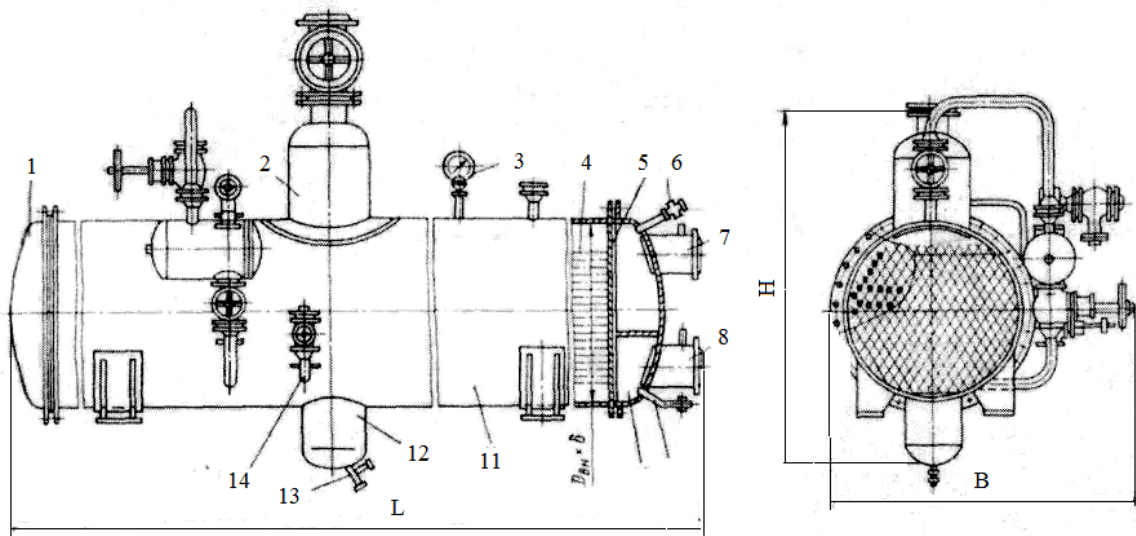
Аміачний кожухотрубчастий випаровувач заповненого типу: 1, 10 - кришки; 2 - сухопарник; 3 - манометр; 4 - труби; 5 - трубна решітка; 6 - вентиль для випуску повітря; 7, 8 - штуцера для введення і відведення розсолу; 9 - злив розсолу; 11 - корпус; 12 - масловідстійник; 13 - кран для видалення мастила; 14 - патрубок для входу рідкого аміаку
